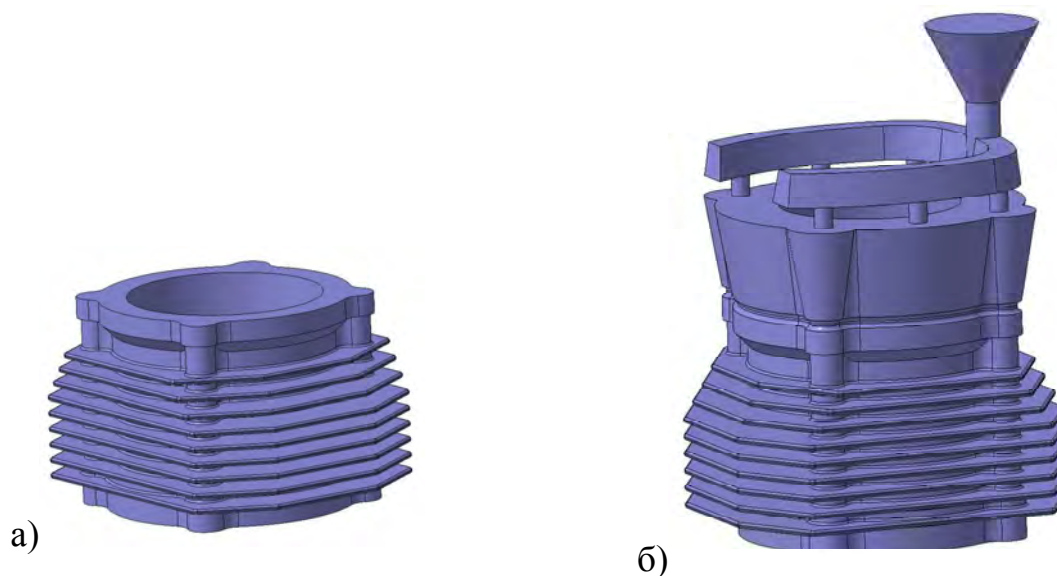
3D-модели: а) отливка «Цилиндр»; б) отливка «Цилиндр» с элементами литниковой системы
